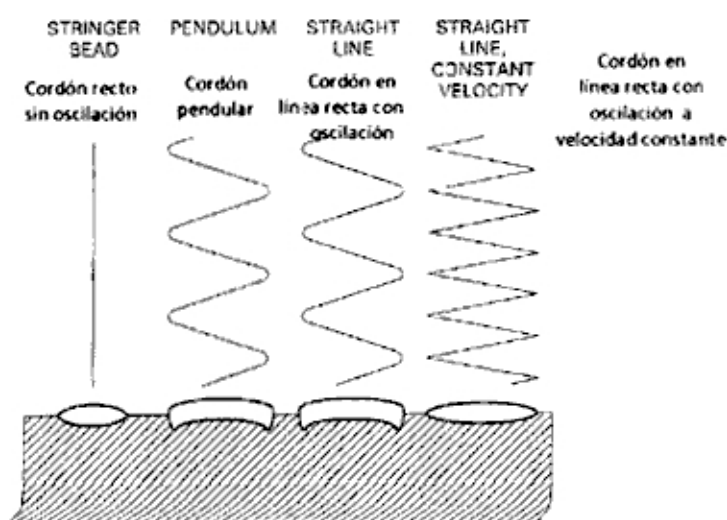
Oscilaciones y Penetración de Cordones de Soldadura y efectos de dilución
